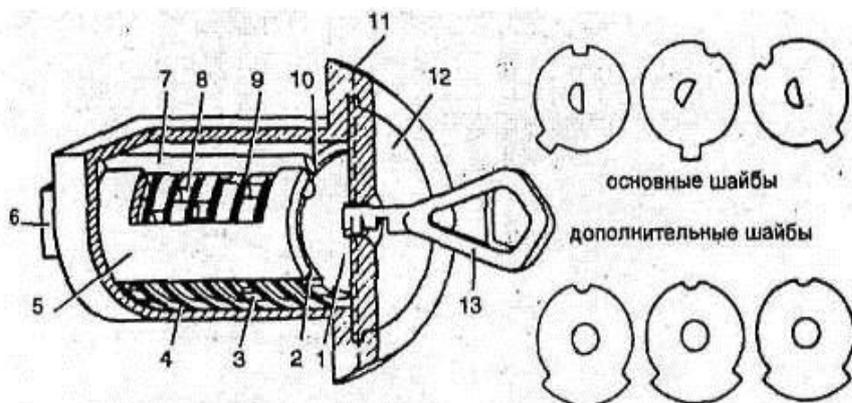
Устройство цилиндрического механизма замка «Аблой»: 1 - основной диск (шайба); 2 - широкий вырез корпуса; 3 - выступ на основном диске; 4 - дополнительный диск (шайба); 5 - корпус; 6 - поводок; 7 - стопорный штифт; 8 - углубление на основном диске; 9 - углубление на дополнительном диске; 10 - узкий вырез в корпусе; 11 - плоскость распила при разборке замка; 12 - ограничительная втулка; 13 - ключ; 14 - корпус блока цилиндрического механизма замка
